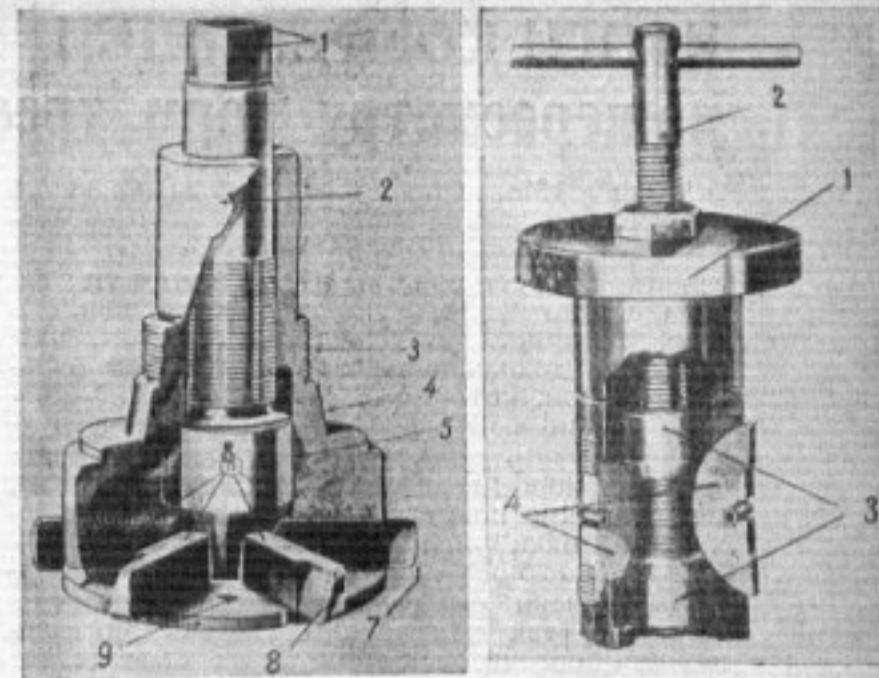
(слева). Резцовая головка и рис. 4 (справа). Центрирующее приспособление
